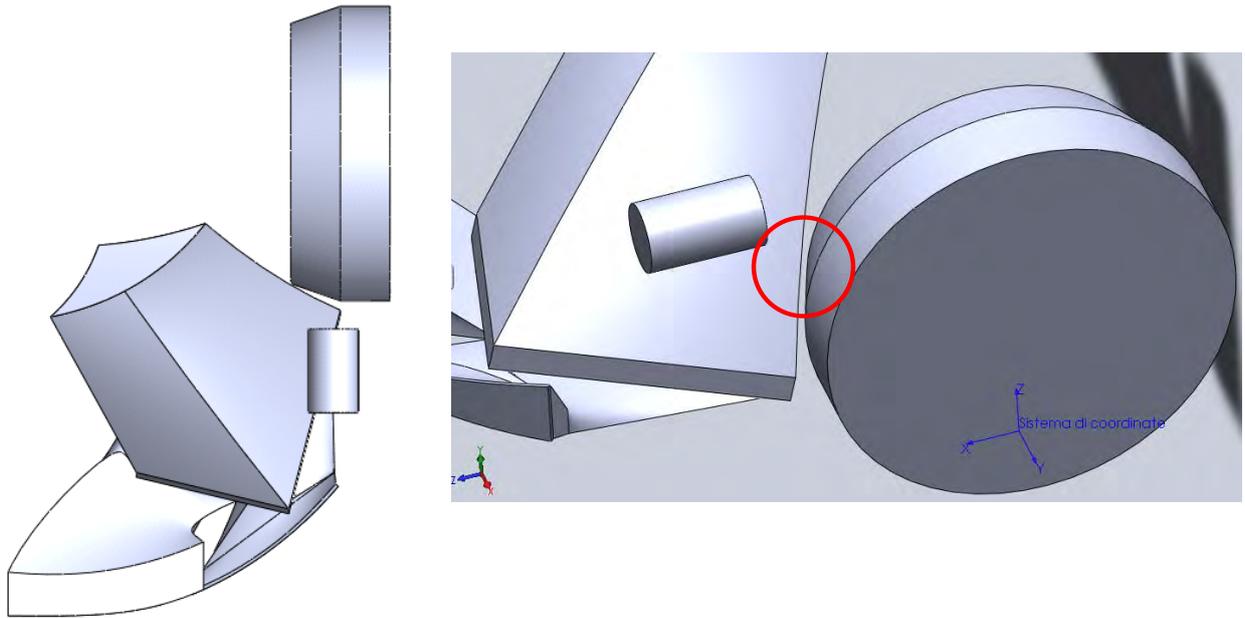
Rappresentazione in pianta della sterzata di 20° della ruota rispetto all'asse di sterzo scelto
